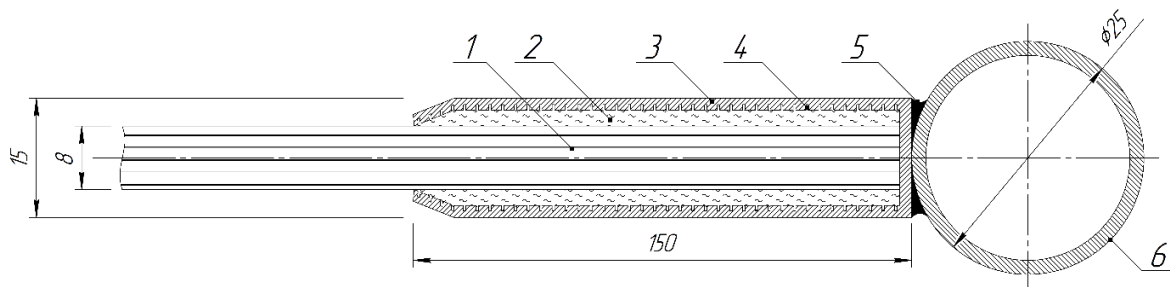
Конструкція муфти для кріплення стержня: 1 – стержень для армування; 2 – двокомпонентна в'язуча сполука; 3 – металева труба типорозміру 15×2,8 мм; 4 – пази; 5 – зварний шов; 6 – кільце для з'єднання муфти з вимірювальним приладом
